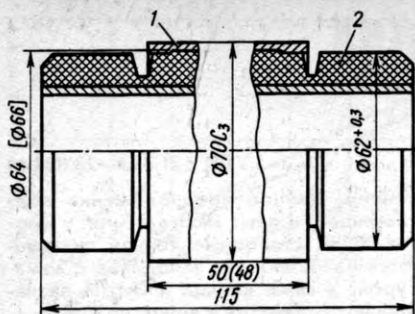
Амортизатор с напрессованной металлической втулкой:
